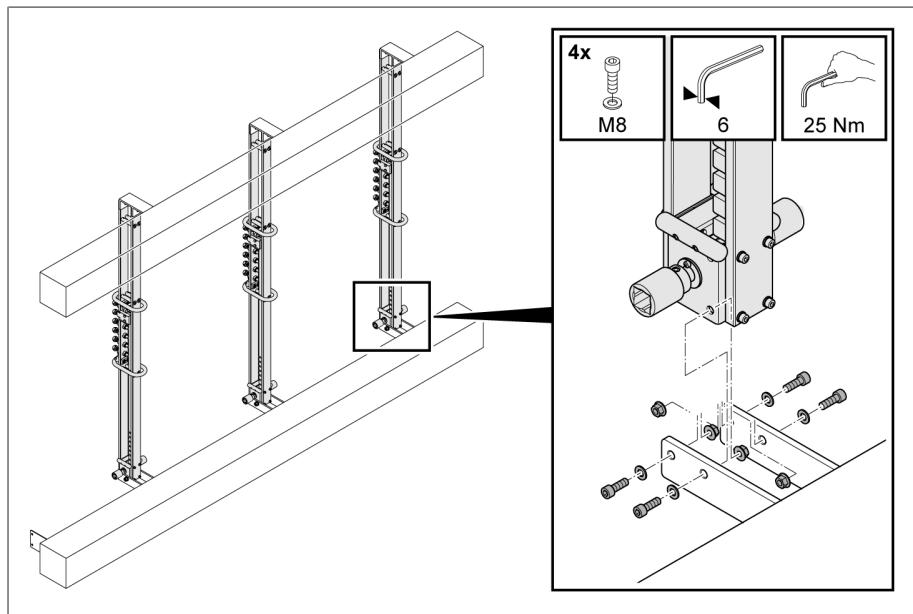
Крепление верхнего редуктора, устройство ПБВ с фронтальным расположением контактов
